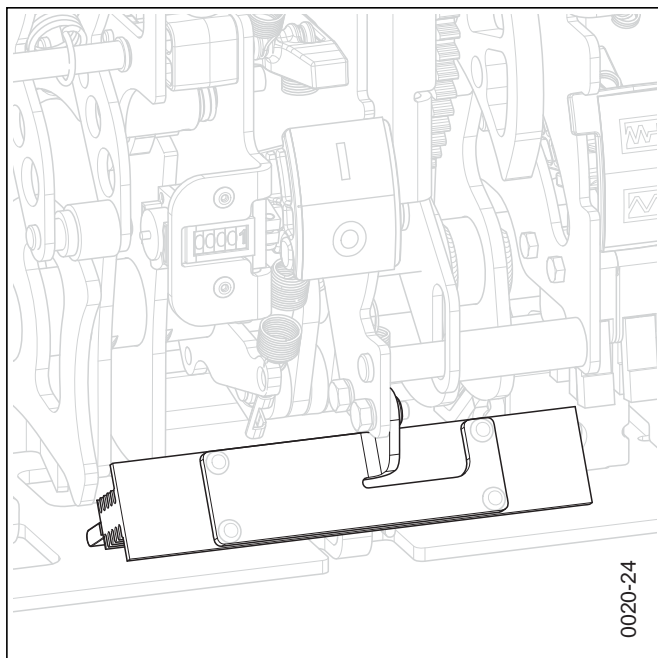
Przykładowy schemat dla przyłączenia wyzwalacza podnapięciowego (-Y7)
